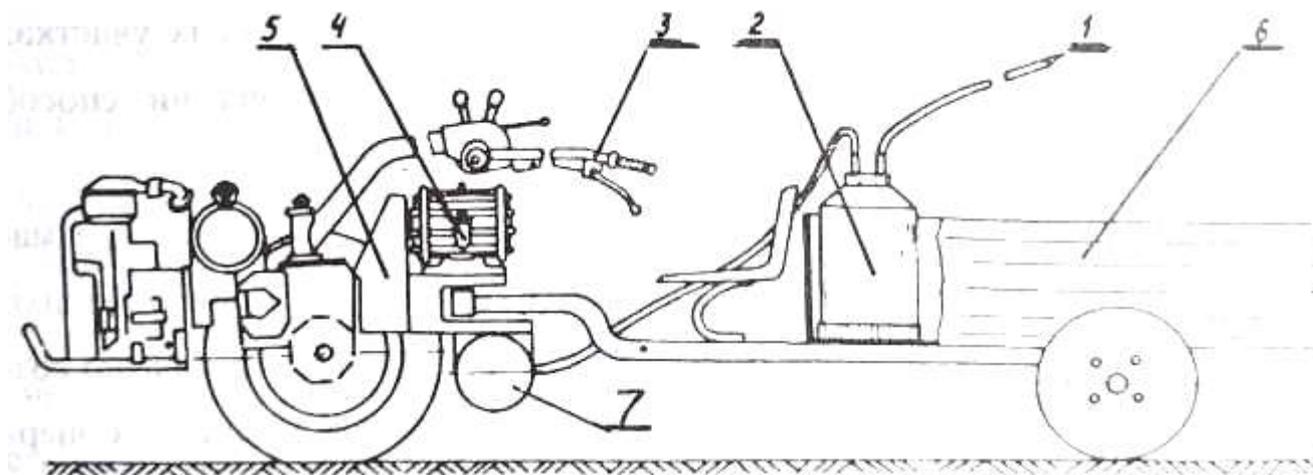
Схема агрегата для пневматической уборки облепихи на базе мотоблока мощностью 5-6 л.с.:
